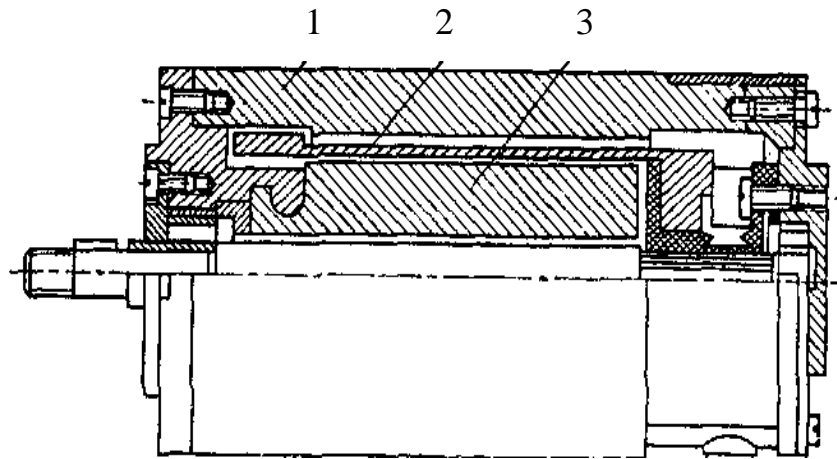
Порожнистий циліндричний якор із звичайною обмоткою
